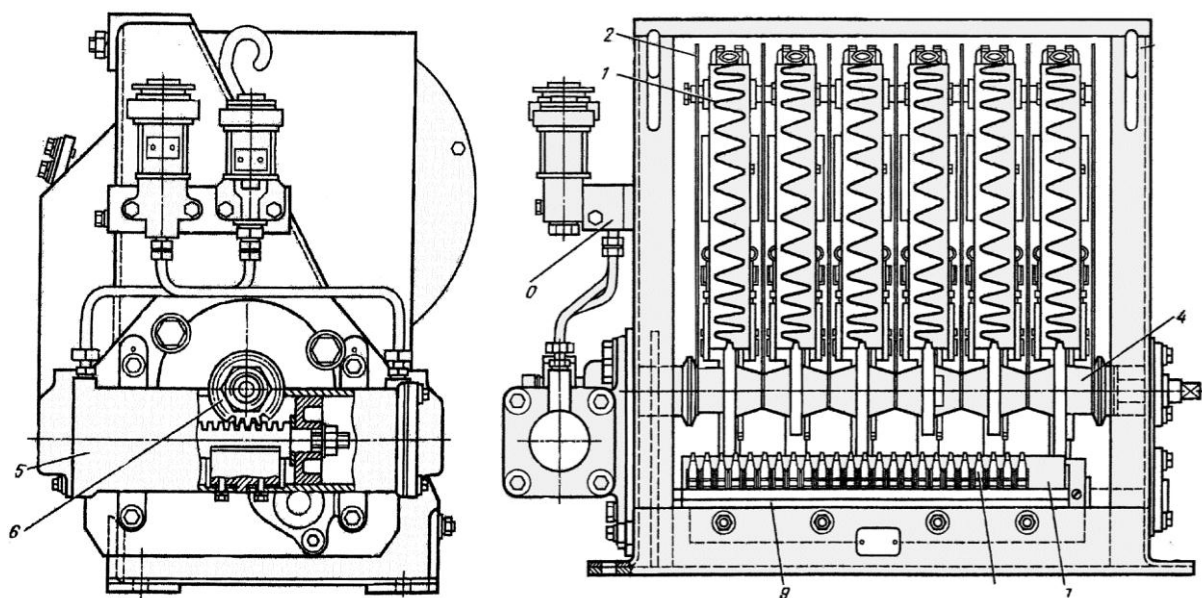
Переключатель кулачковый групповой ПКГ-040-01
